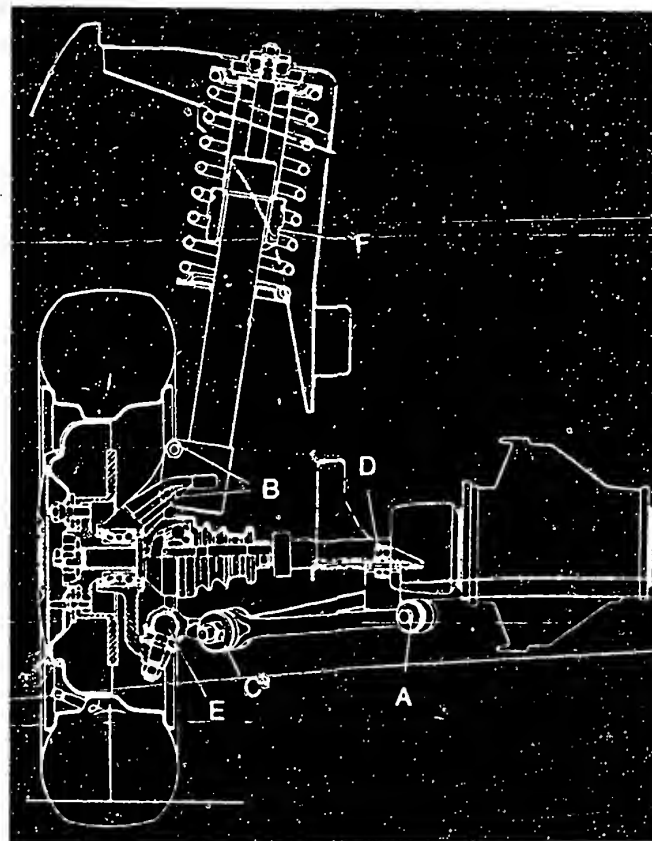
Einzelteile der Vorderradaufhängung: A Querlenkerlagerung – B Querstabilisatorlager – C Zugstangenbefestigung – D Stossdämpferbefestigung – E Aufschlaggummi des Federbeins.
